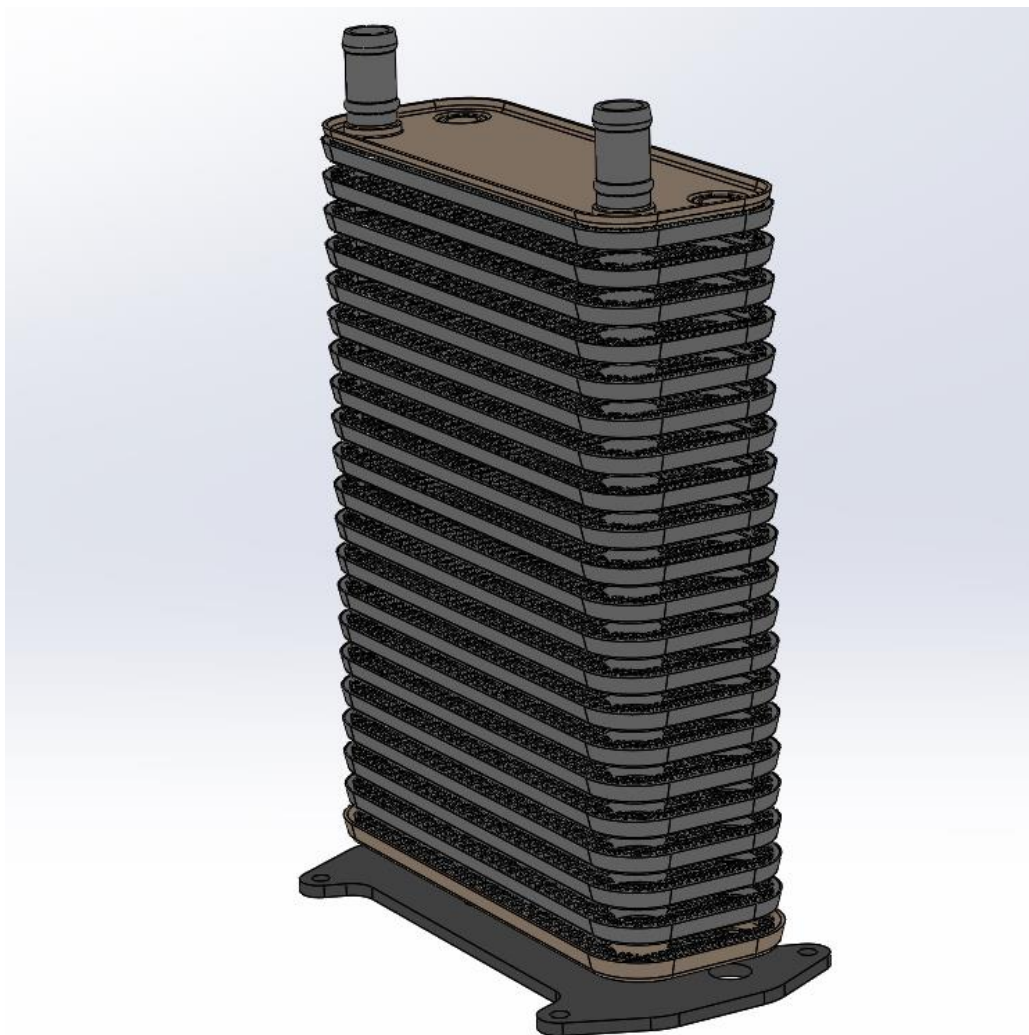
Schimbător de căldură în plăci brazate vedere explodată
